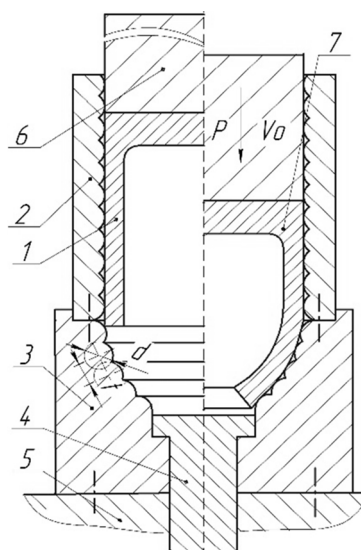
Схема обтиску порожнистої заготовки в контейнері і матриці спеціального профілю
